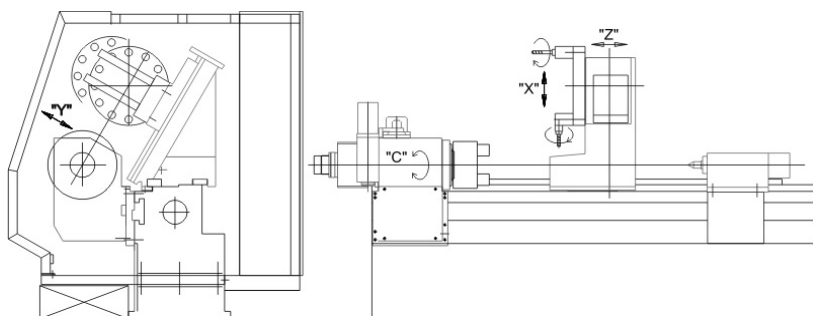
Центр токарный с устройством позиционирования и круговой подачи шпинделя (осью С), револьверной головкой с осью Y для токарного и приводного инструмента
